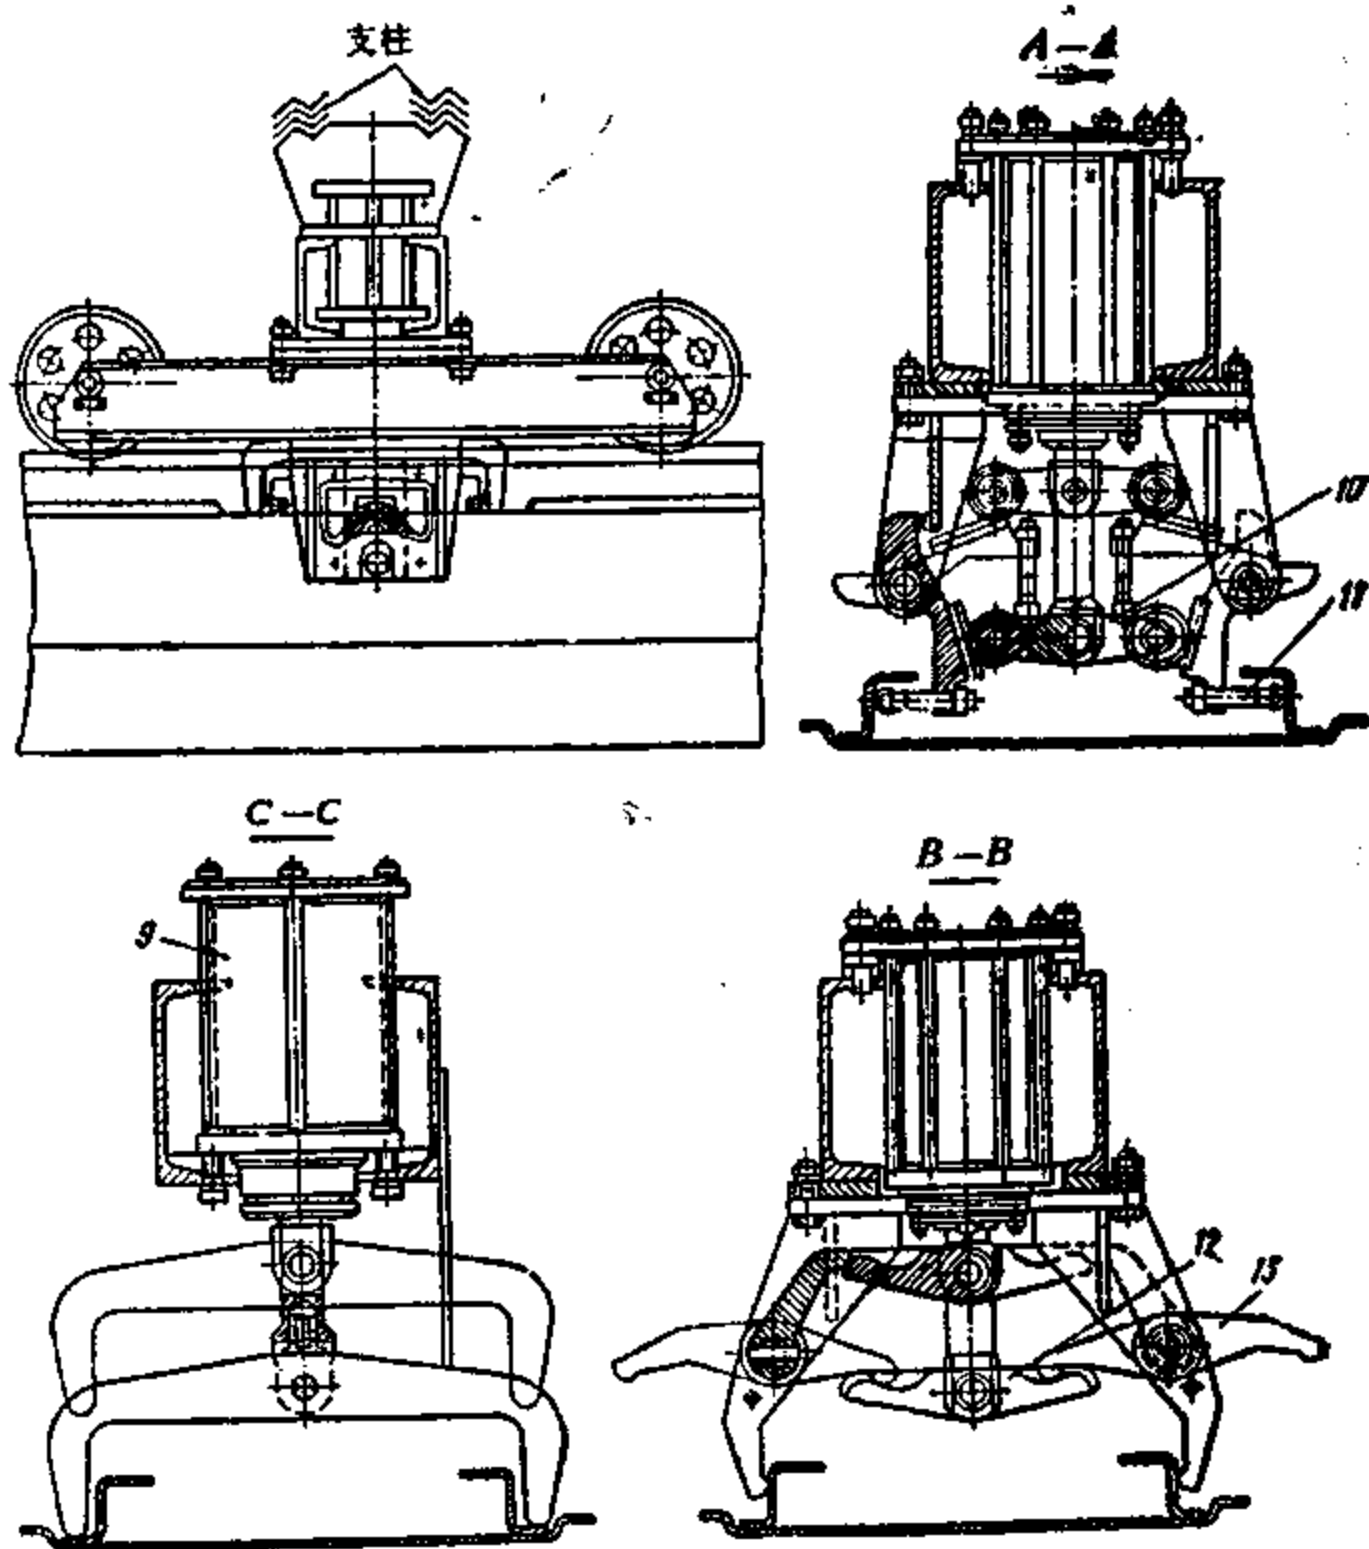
机械化装配焊接客车平面构件的装置
